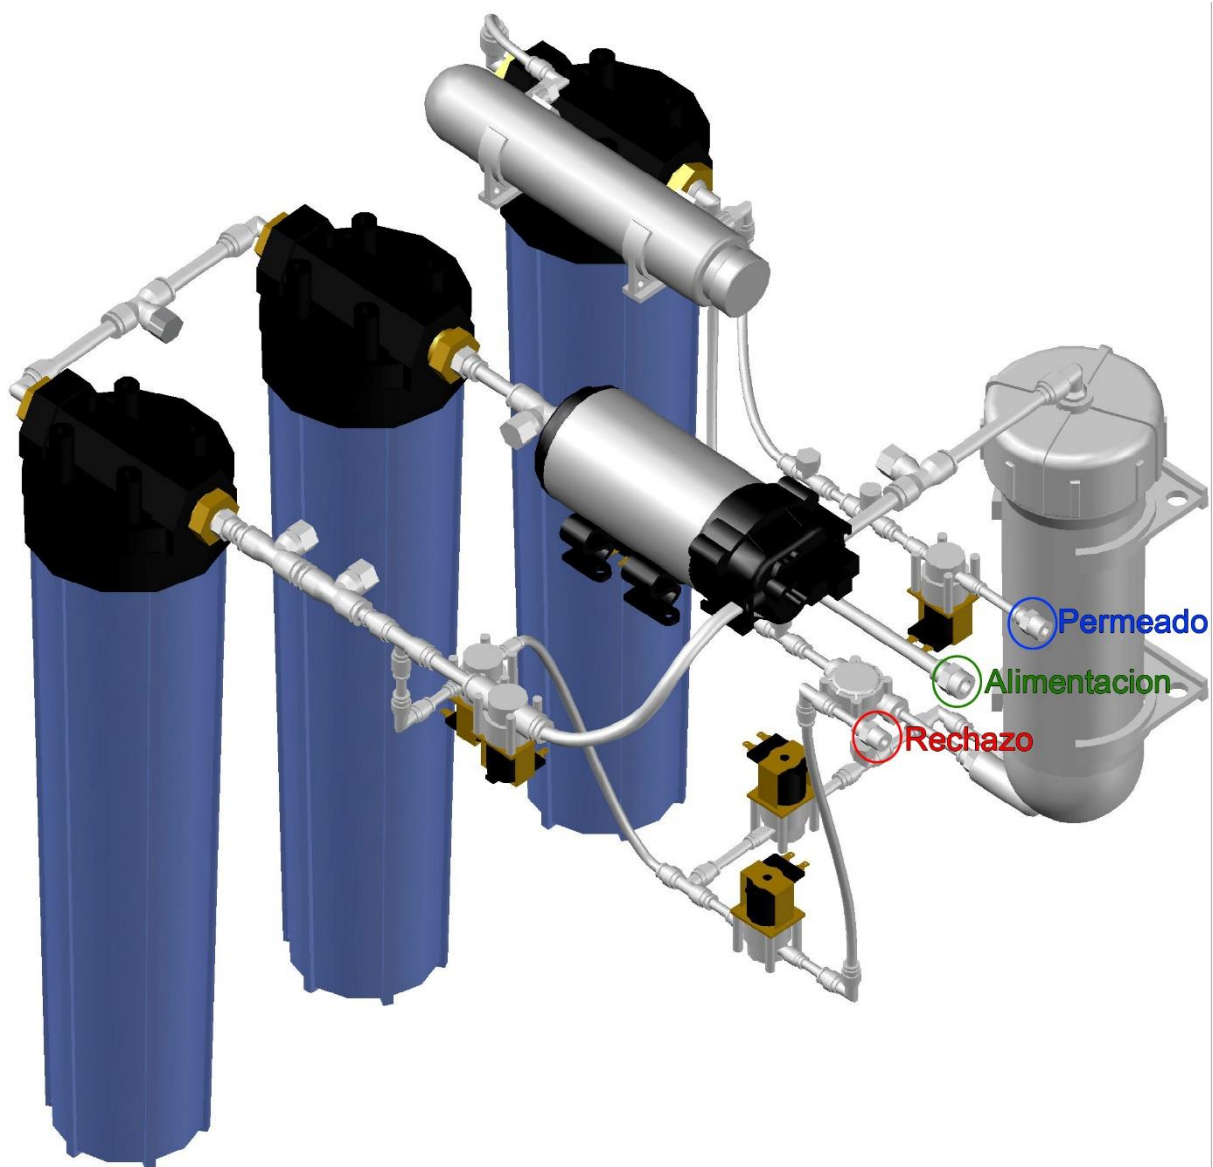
Representación 3D del esquema general de la planta (Vista trasera-lateral).
